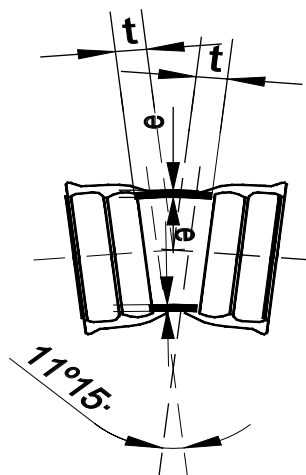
Esquema de dimensiones de codo de 1/16 de doble extremo campana (sin escala)
